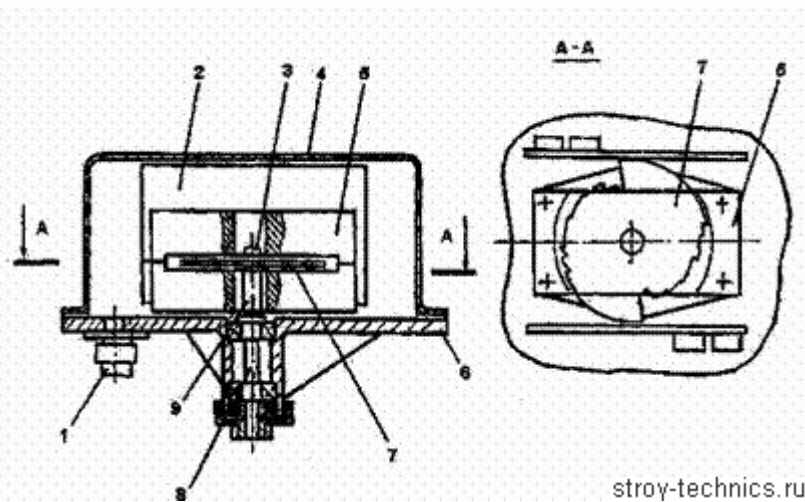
Датчик длины телескопической стрелы: 1 — разъем; 2 — плата преобразователя; 3 — винт; 4 — крышка; 5 — блок катушек; 6 — основание; 7 — экран; 8 — подшипниковый узел; 9 — ось.
